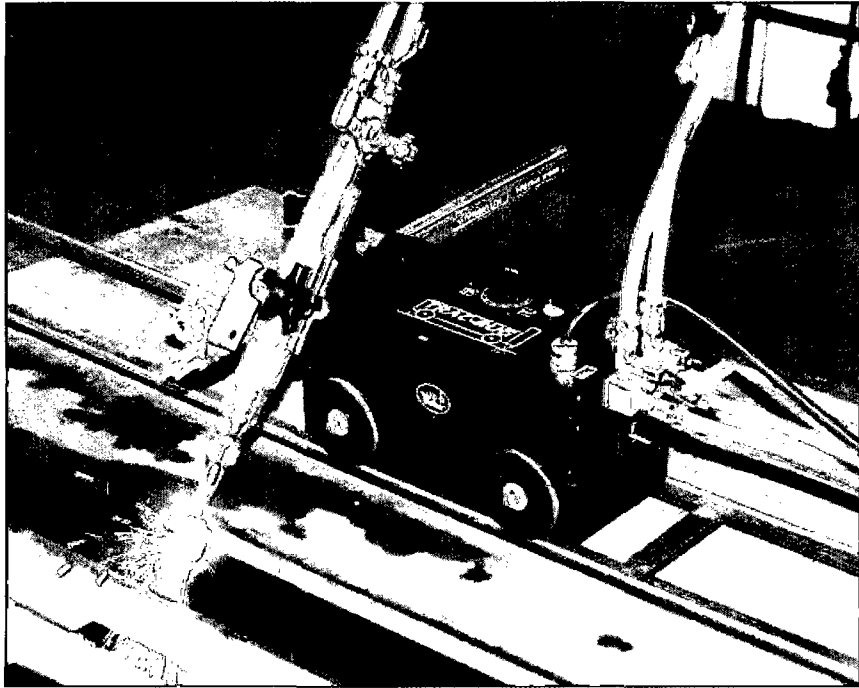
Máquina de soldadura y corte por Oxy-Fuel o Plasma TRAC-BUG de la empresa BUG-O Systems[12].
